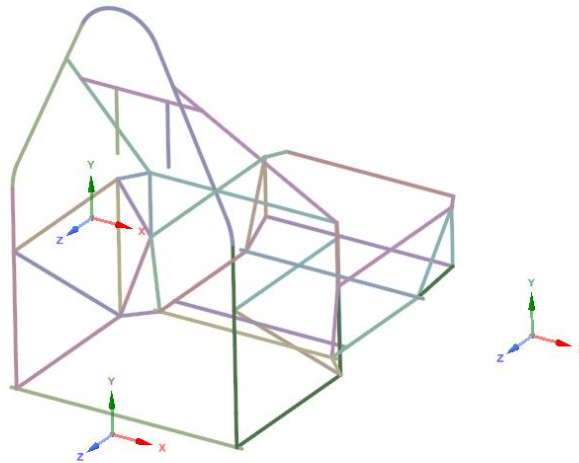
Geometría de la parte tubular preparada en *Static Structural-SpaceClaim*.
